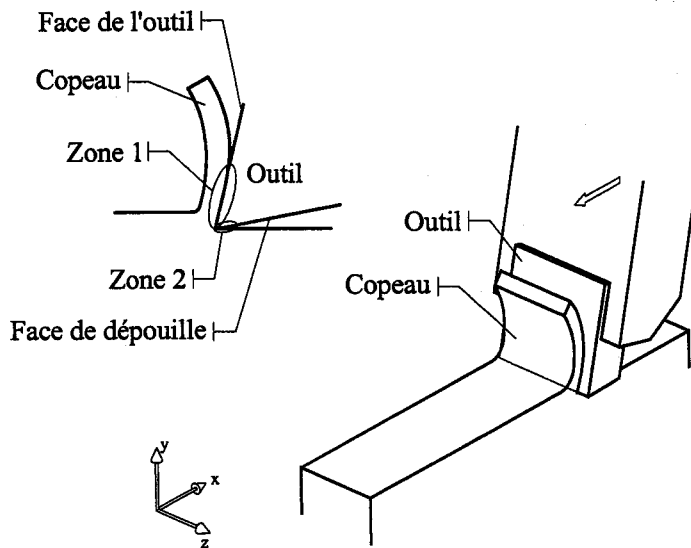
Coupe orthogonale – Mise en évidence des zones de frottement entre l'outil et la pièce pendant l'usinage, Bailey [59].
